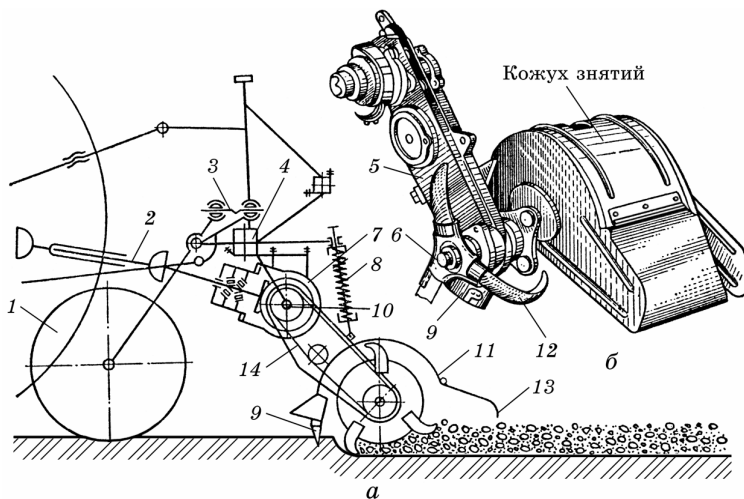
Культиватор фрезерний КФ-5,4:
